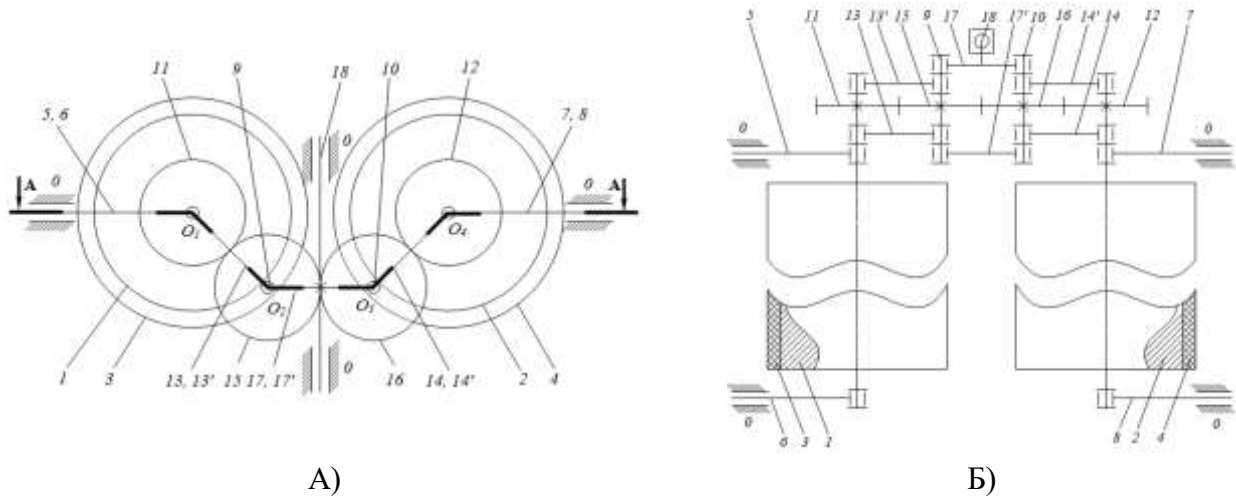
Зубчато-рычажный дифференциальный передаточный механизм с симметричным перемещением центров вращения ведущих и ведомых зубчатых колес
